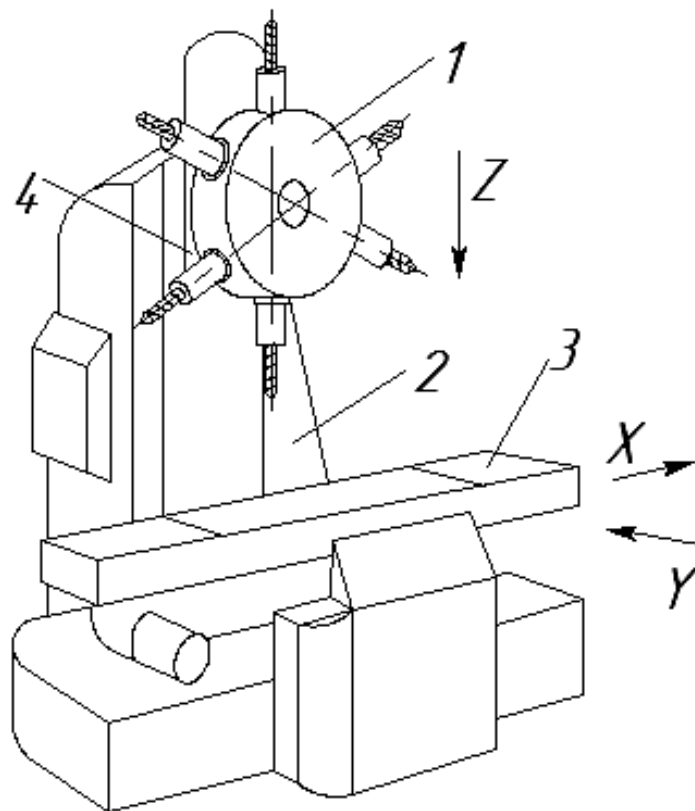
Загальний вигляд вертикально-свердлильного верстата з ЧПК і револьверною головкою
